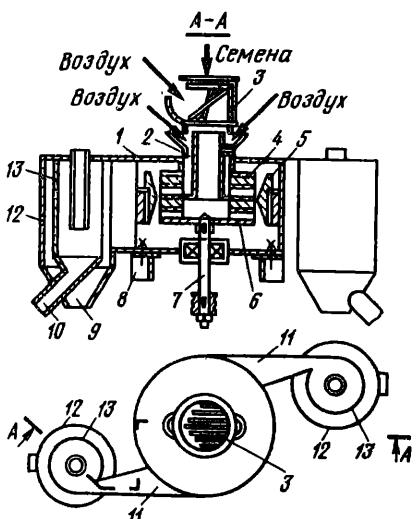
Схема центробежной обрушающей машины РЗ-МОС:
